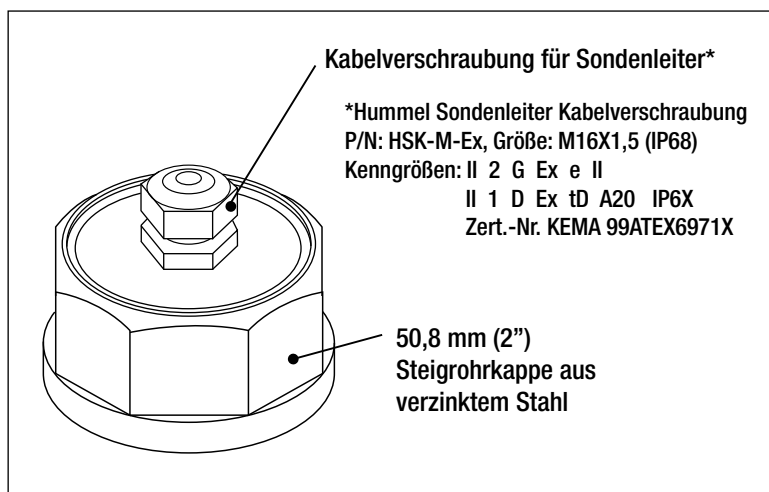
51 mm Steigrohrkappe mit Gewinde Montage P/N 705-100-2203
